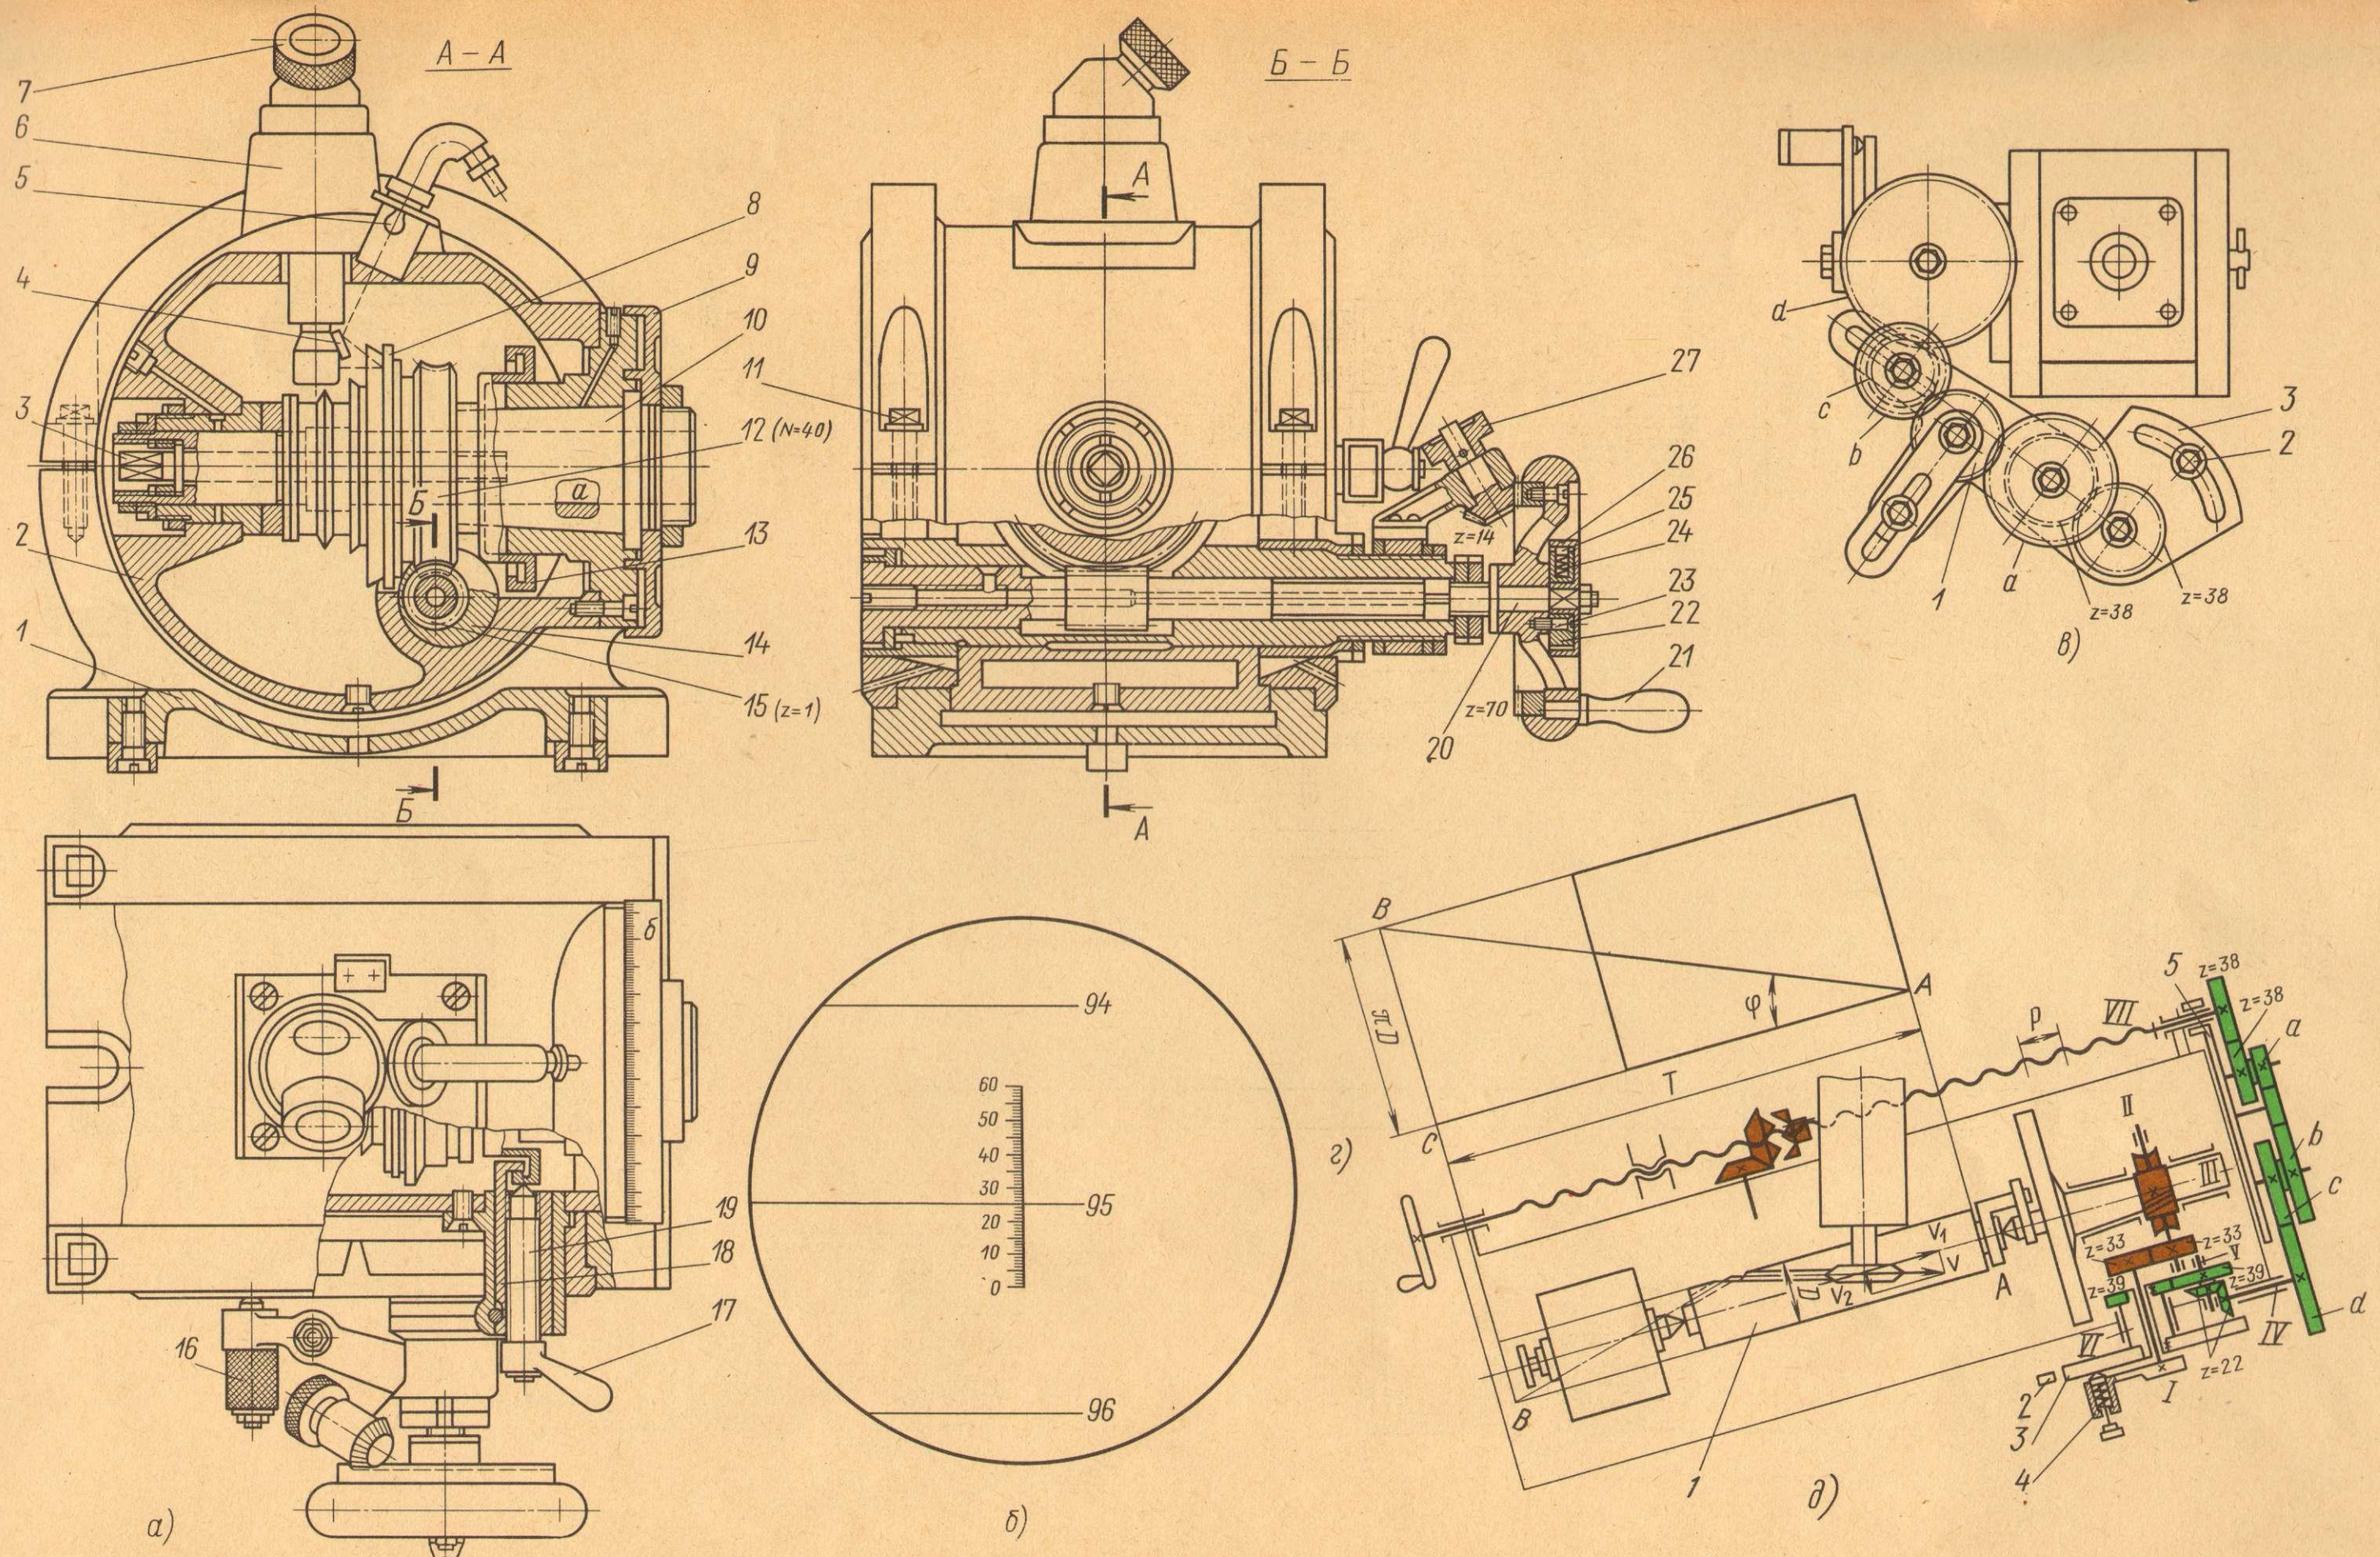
Оптическая делительная головка. Схема настройки станка и универсальной делительной головки для фрезерования винтовых канавок
